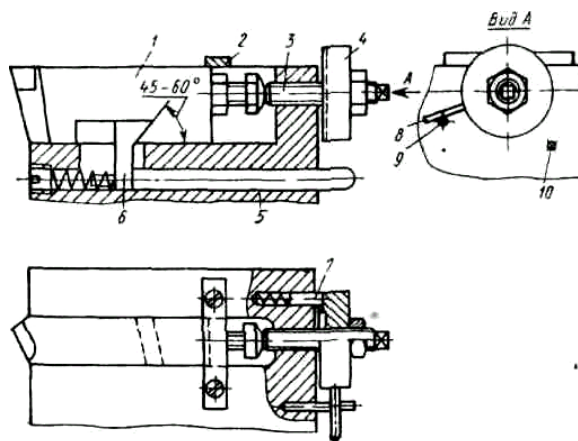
Пристрій для ручного підстроювання різця. 1 - різець, 2 - запобіжна планка, 3 - мікрометричний гвинт, 4 - храпове колесо, 5 - різцетримач, 6 - гачок, 7 - засувка, 8 - ручка храпового колеса, 9 і 10 – штифти
